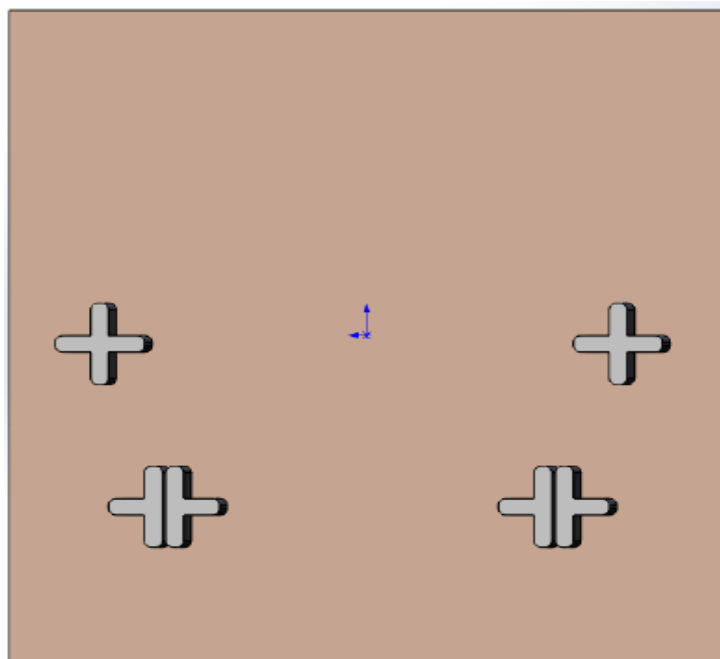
Пластина для припаювання тонкої полоски (фольги)
